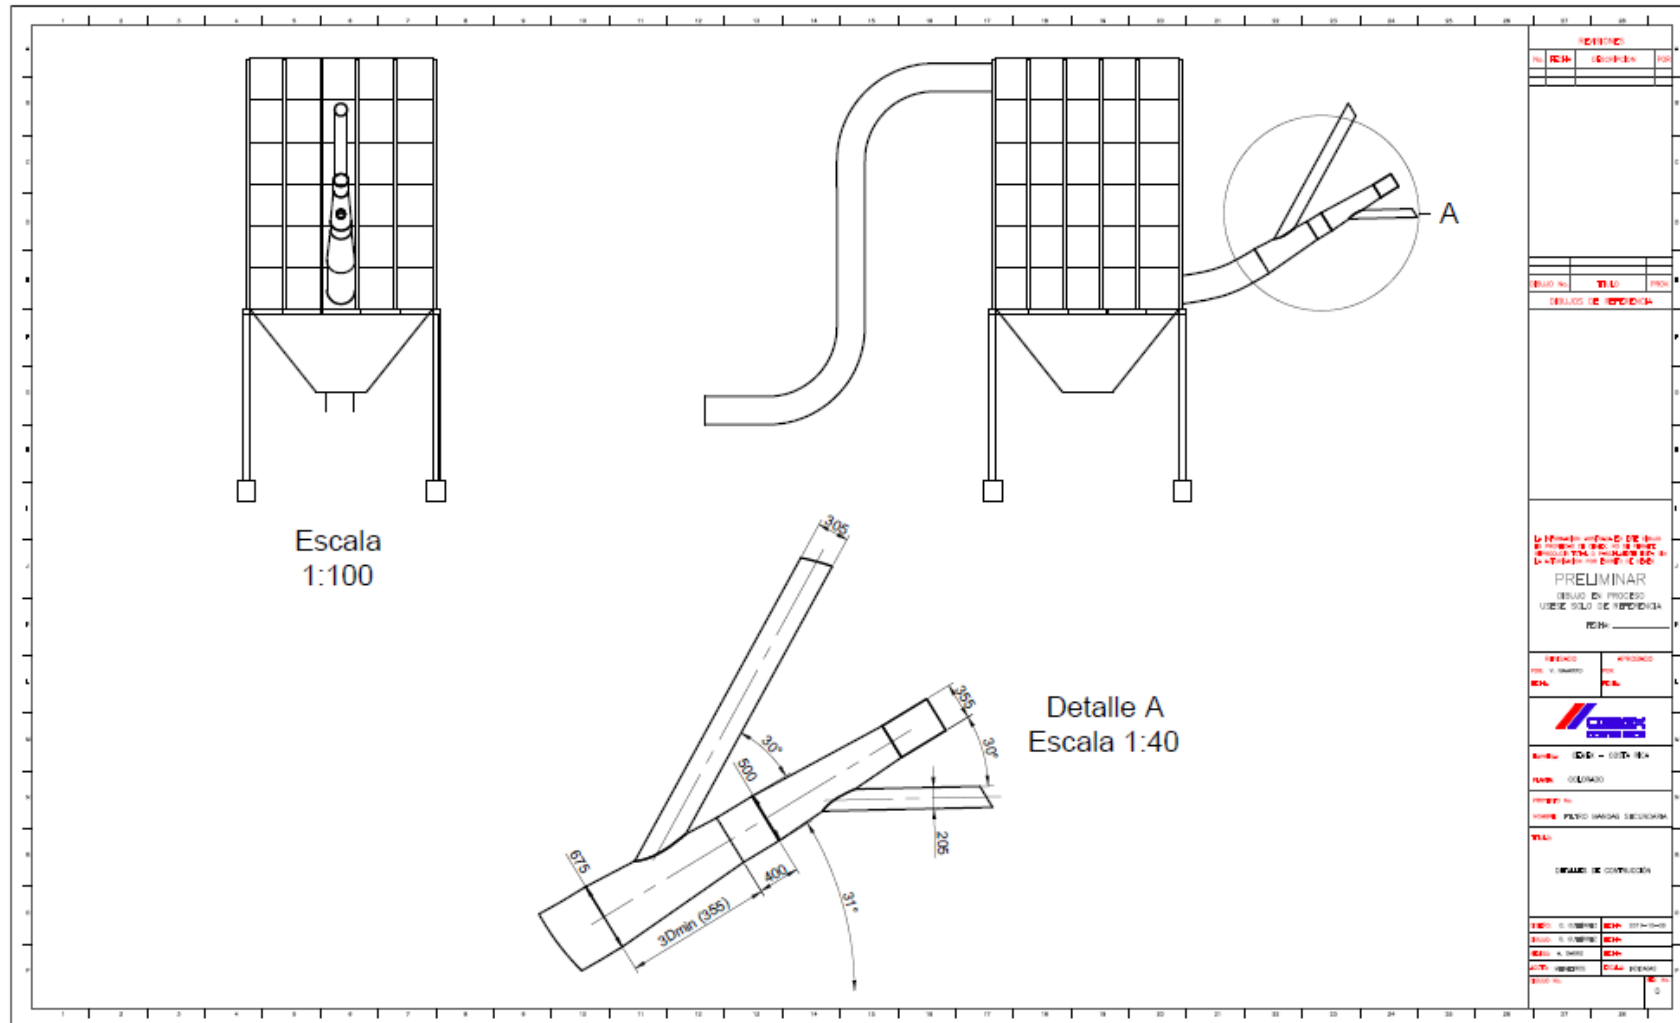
Detalles de conexión de tuberías ideal con prevista a la entrada del filtro.
